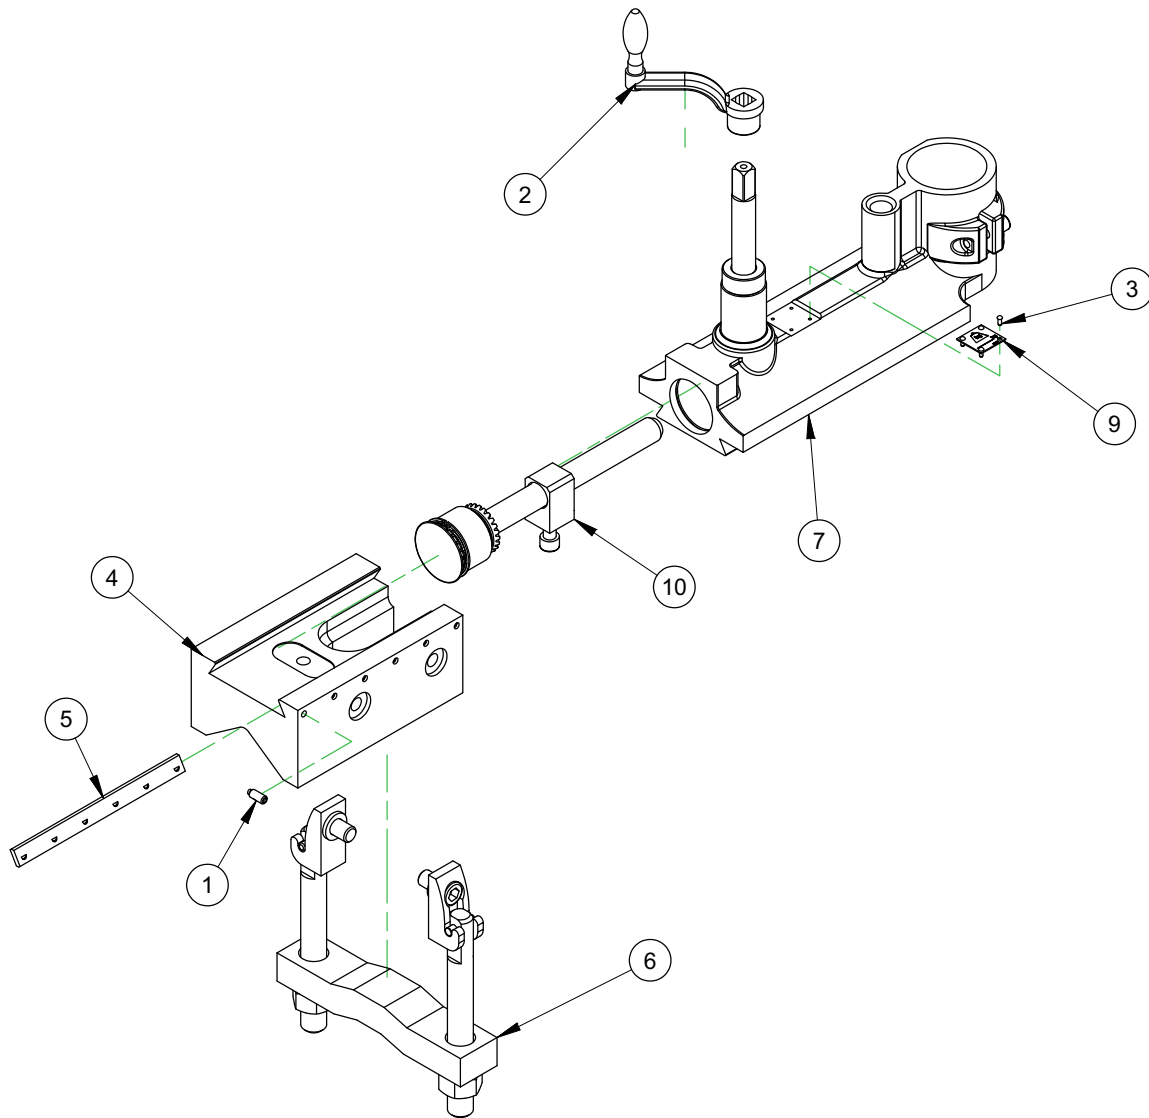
CONJUNTO DE FRESADORA HIDRÁULICA DE 4ª GENERACIÓN (N/P 34933)
